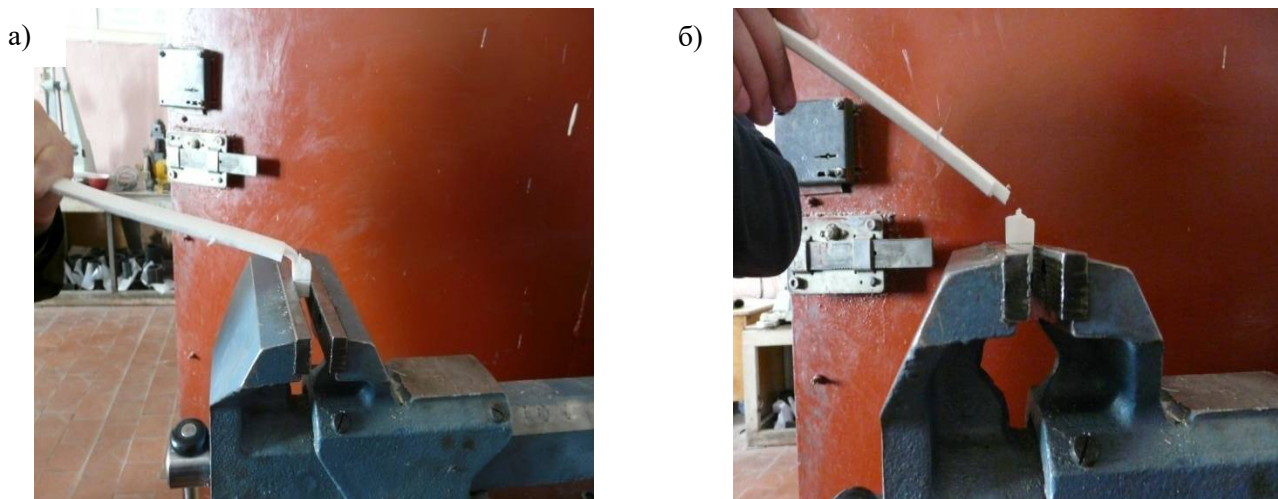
Общий вид испытаний на отдрив образцов сварных соединений:
